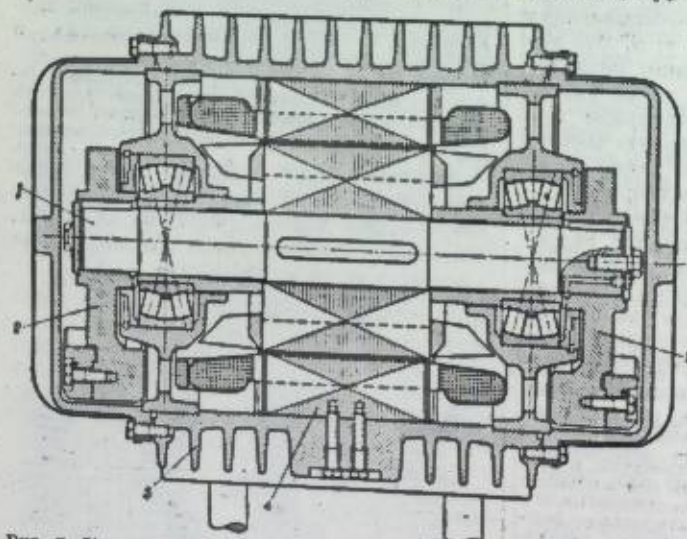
Конструкция вибратора вибромолота: 1 — ротор, 2 — дебалансы, 3 — корпус, 4 — электродвигатель.
